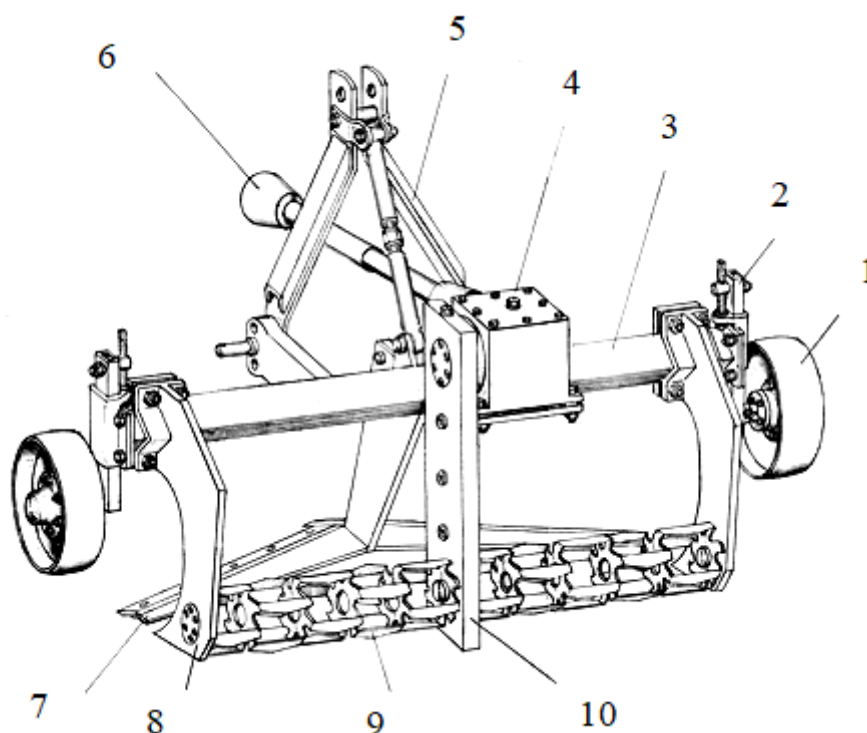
Схема комбинированного подпокрывного фрезерователя
